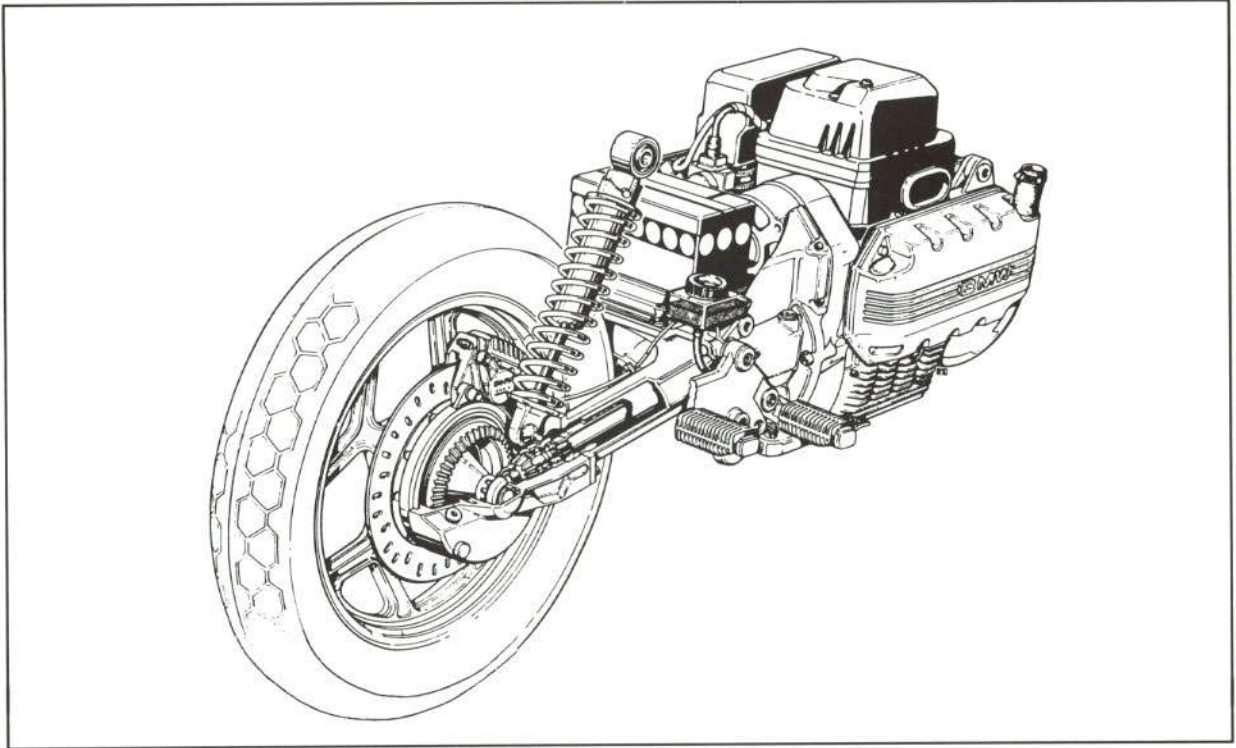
Anclaje de motor a chasis. BMW K-100.
